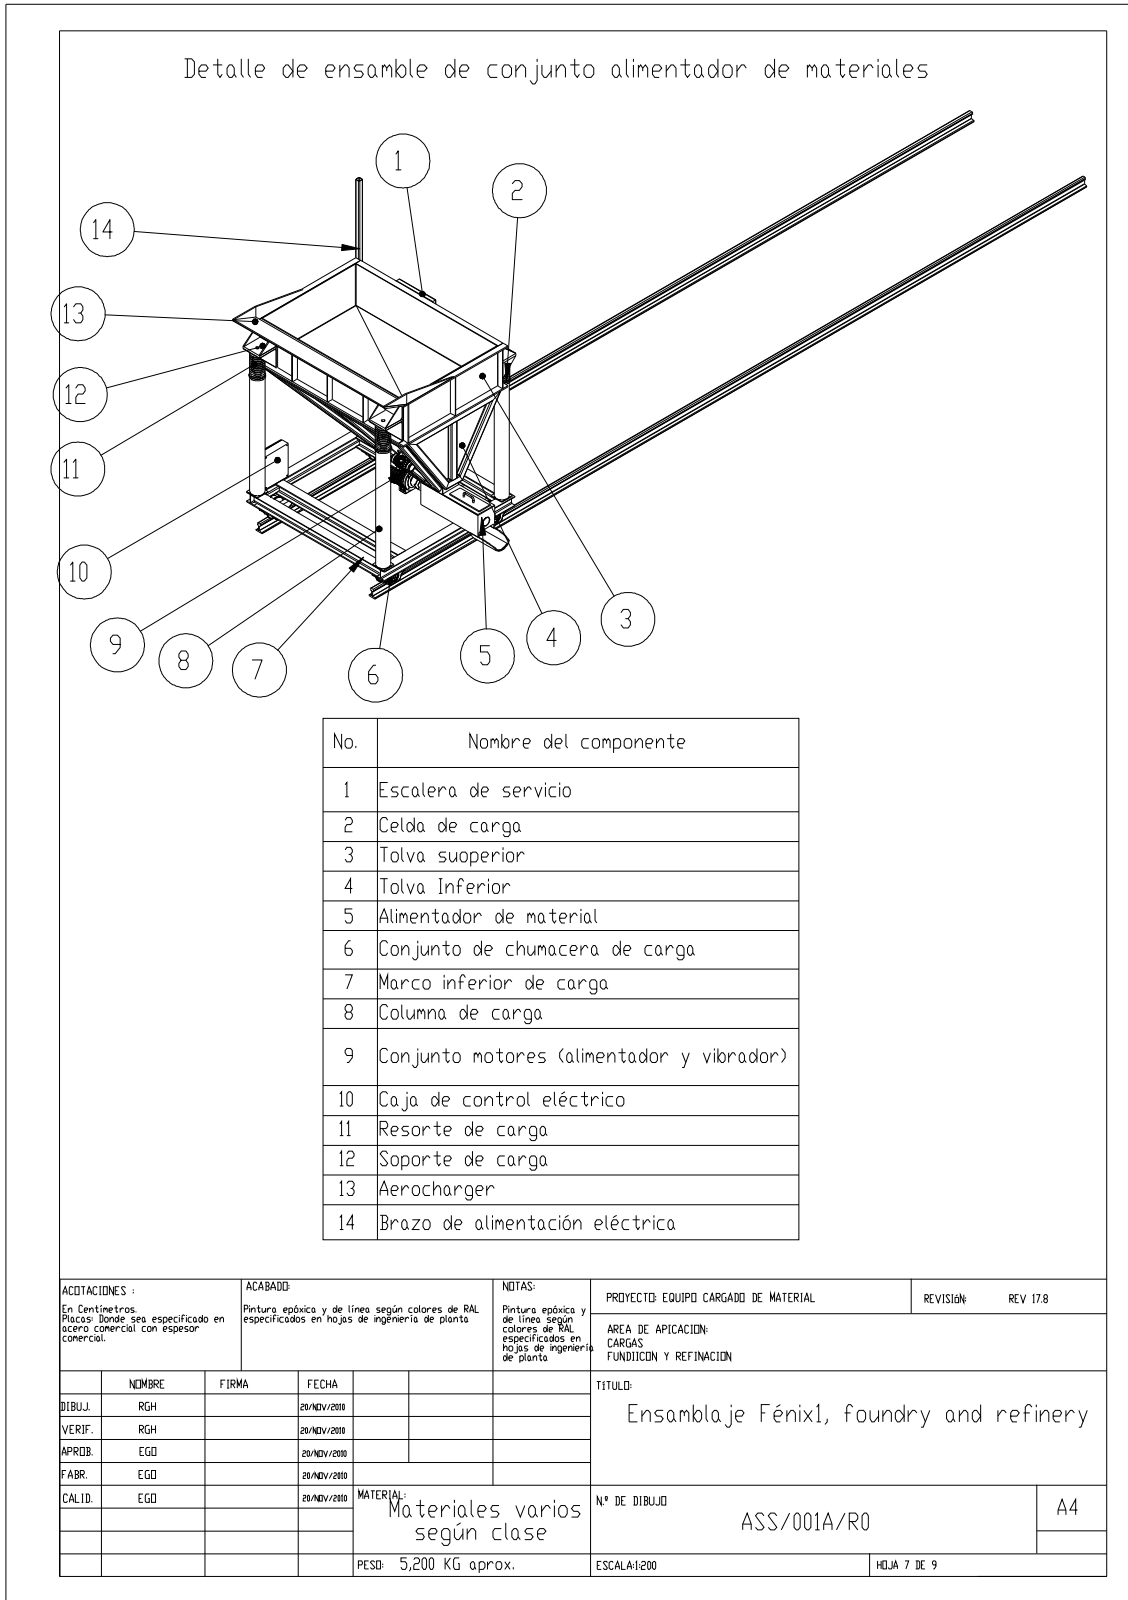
Despiece general de la unidad cargadora de material (detalle de ensamble).
